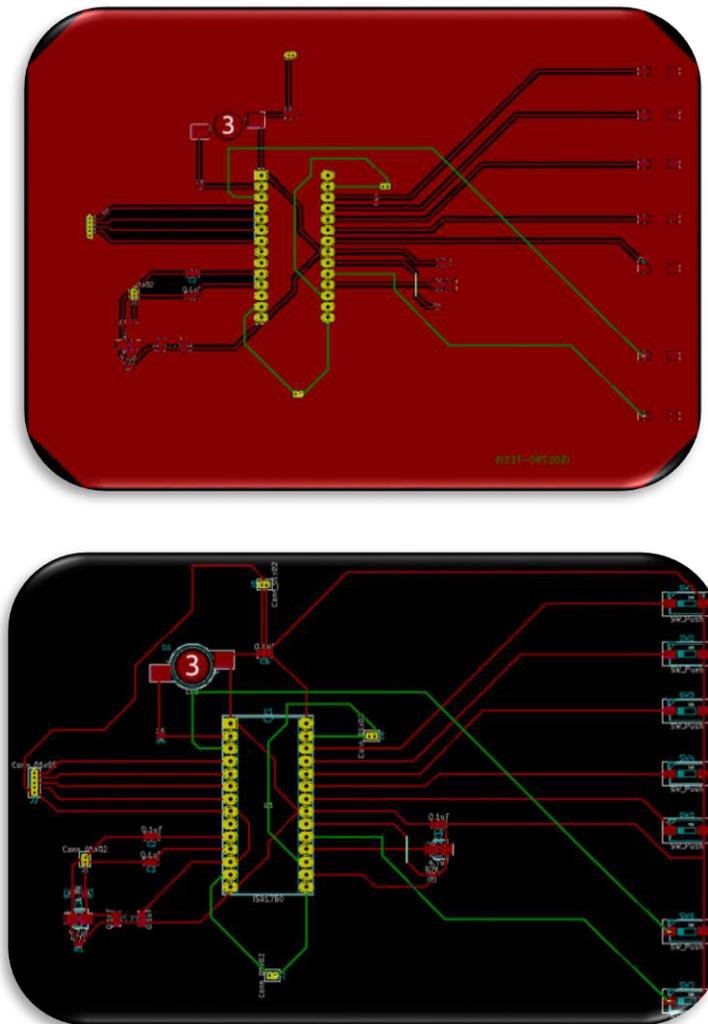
Diseño del PCB en el programa KiCad del ISD1760.
